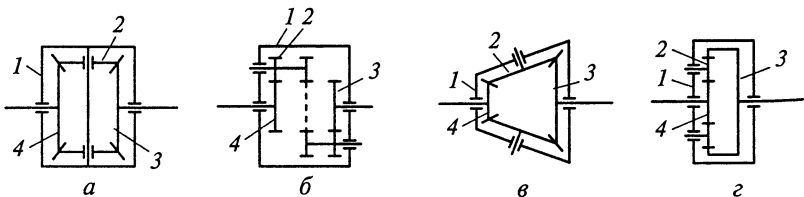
Кинематические схемы шестеренных дифференциалов: а, б — симметричных; в, г — несимметричных; 1 — корпус; 2 — сателлит; 3, 4 — шестерни
